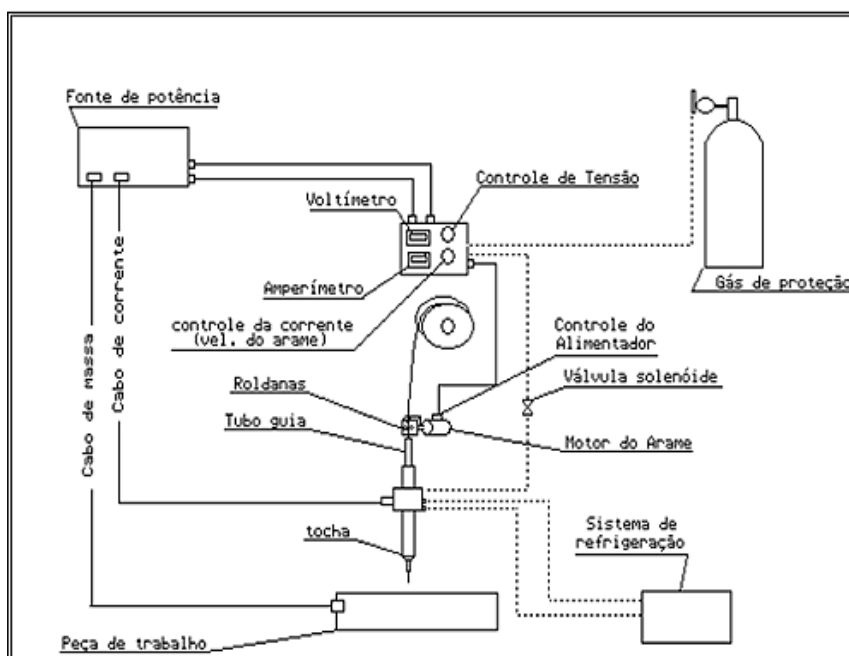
Equipamento básico para soldagem com arame tubular [AWS, 1991]
